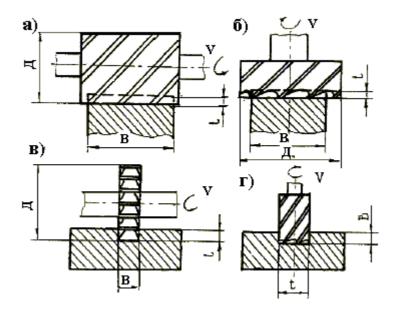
Виды фрезерования: а) фрезы цилиндрические; б) фрезы торцевые; в) фрезы дисковые; г) фрезы концевые.
